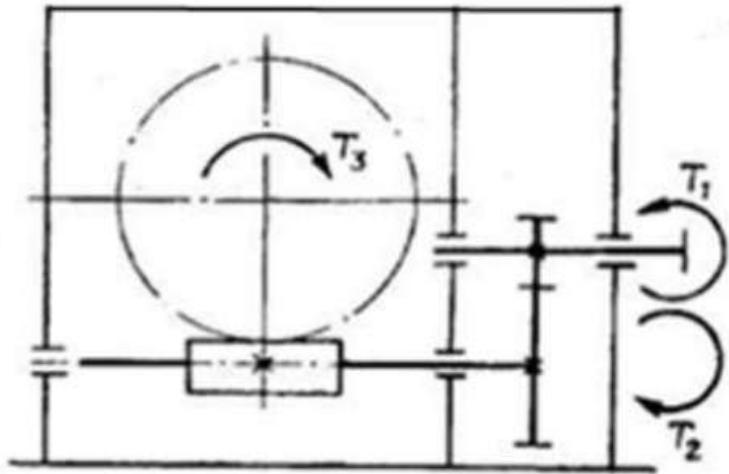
Крутящие моменты в цилиндрическо-червячном редукторе
